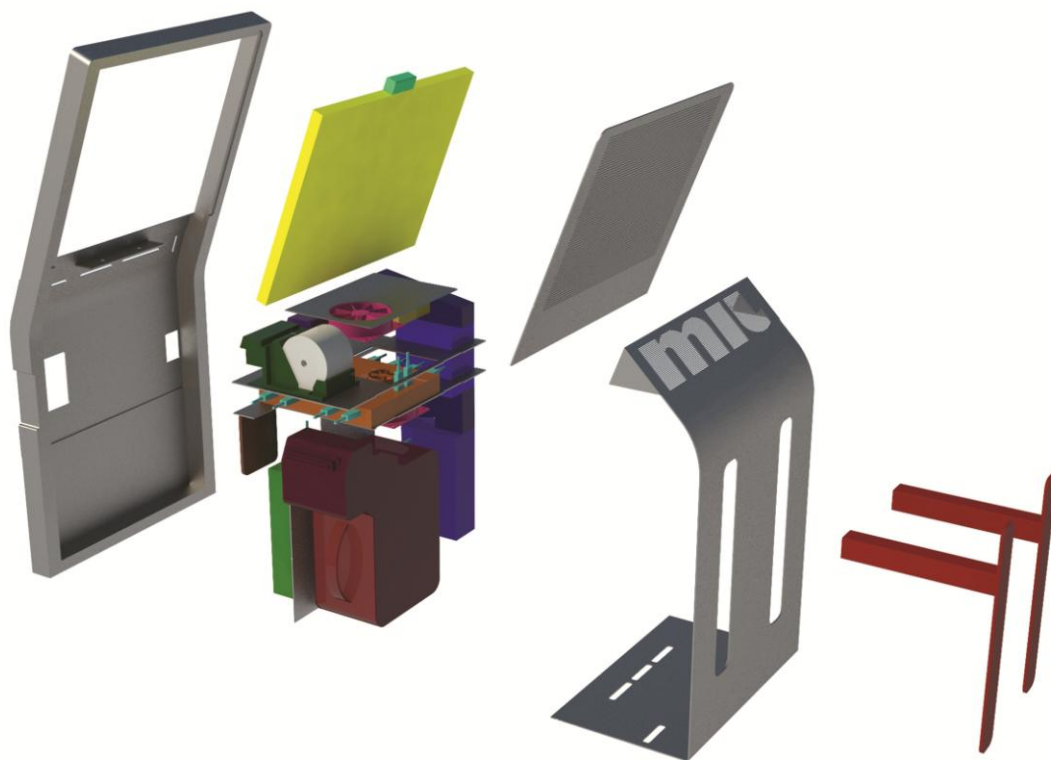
Obslužný kiosk - výměna peněžních boxů
